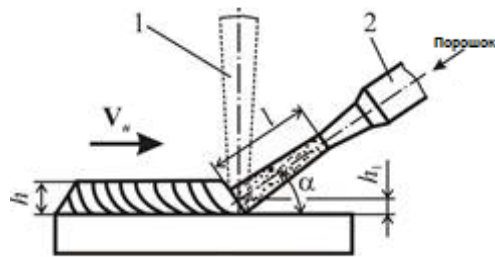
Схема процесу газопорошкового лазерного наплавлення:
